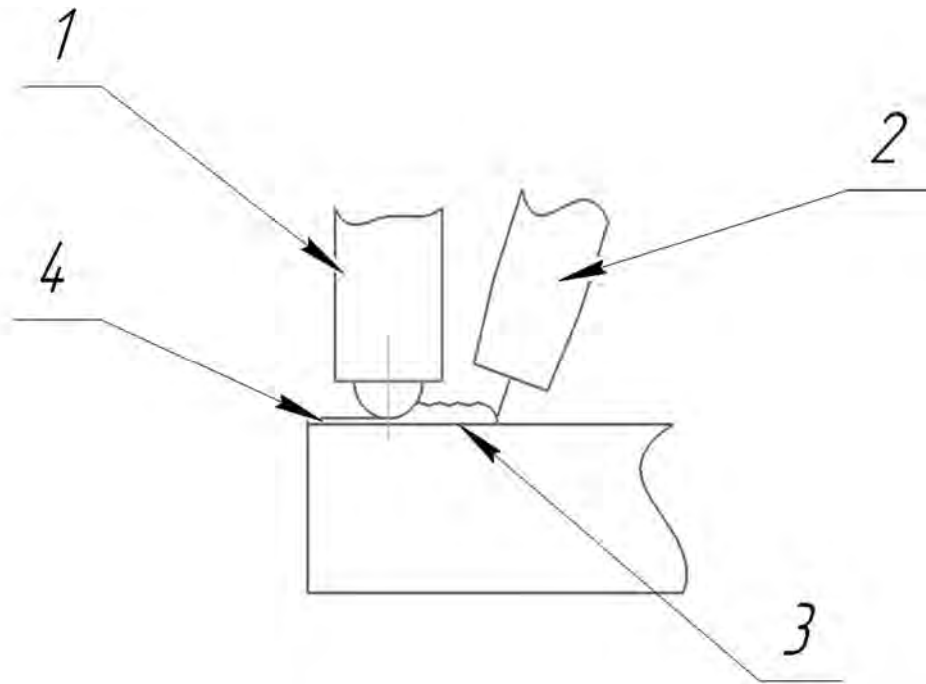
Схема объединённого процесса сварки алюминия
